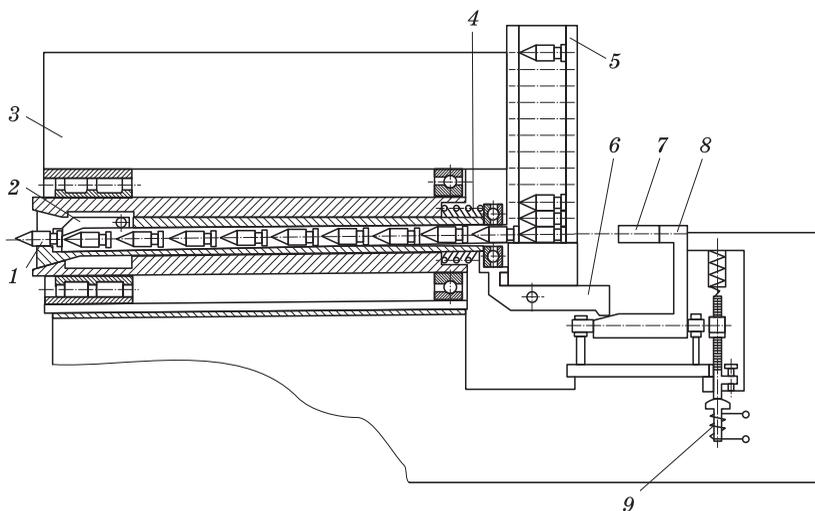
Схема устройства для автоматической замены зубозакругляющих фрез
